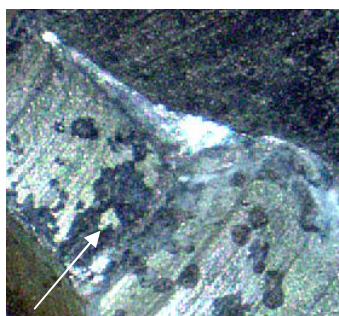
Внутренняя поверхность корпуса стержневого пломбирочного устройства. Смещение металла показано стрелкой
